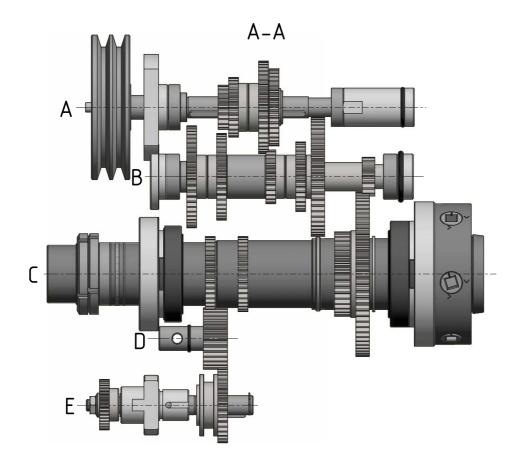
Getriebe Spindelstock 2-6 - Headstock gear 2-6
